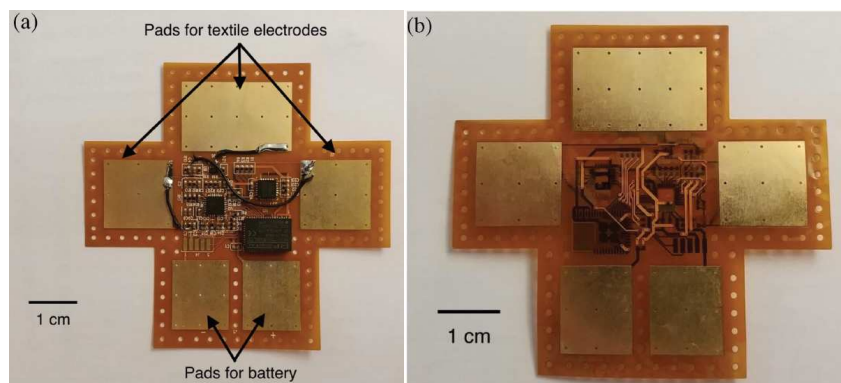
Photos du PCB flexible. (a) Face avant. (b) Face arrière.
